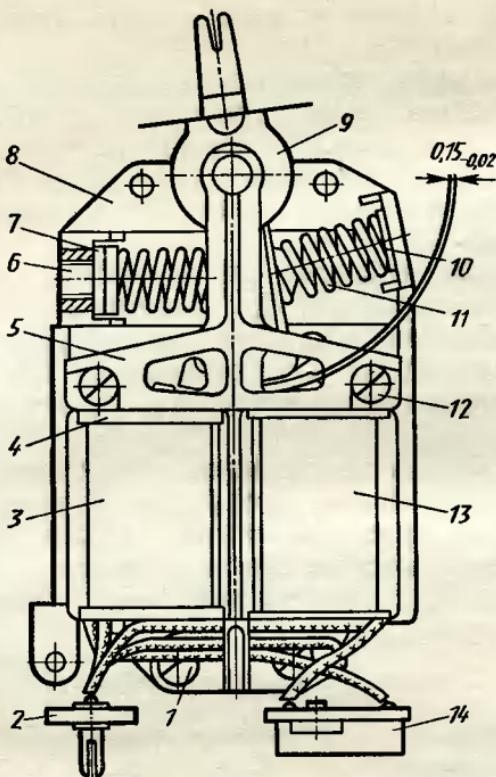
Электромагнитный привод бритвы «Оксамит-80»:
